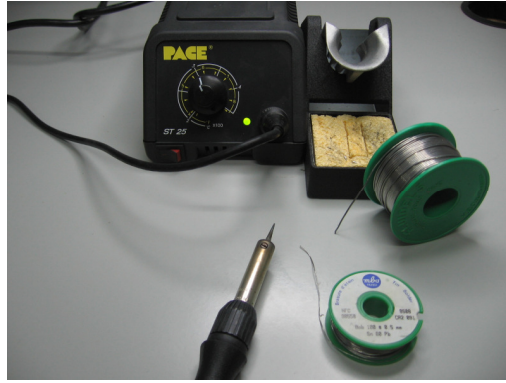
Estaño y soldador para realizar la soldadura de los componentes al circuito.
